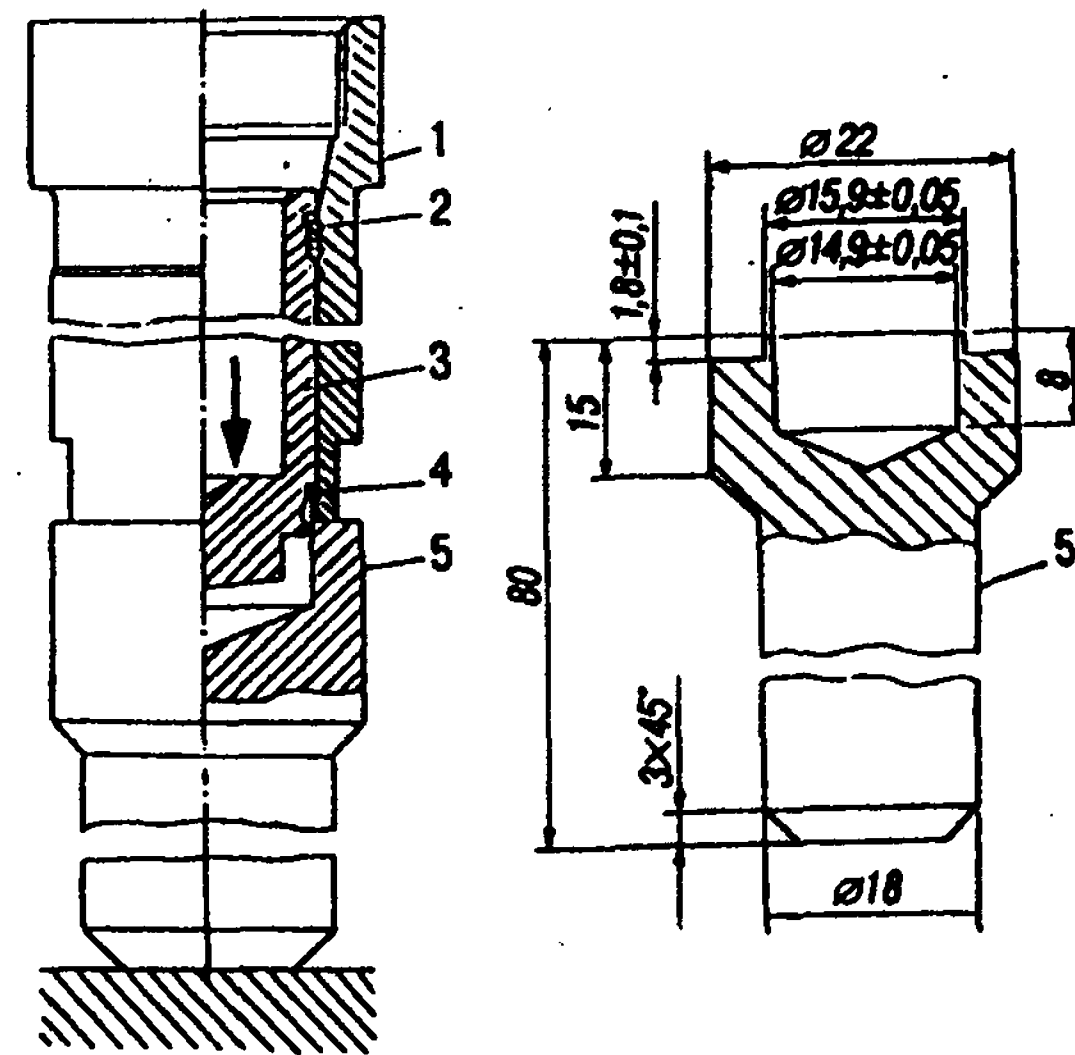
Фиксация («зарядка») корпуса и плунжера гидронатяжителя с помощью оправки: 1 - корпус; 2 - запорное кольцо; 3 - плунжер; 4 - стопорное кольцо; 5 - оправка
